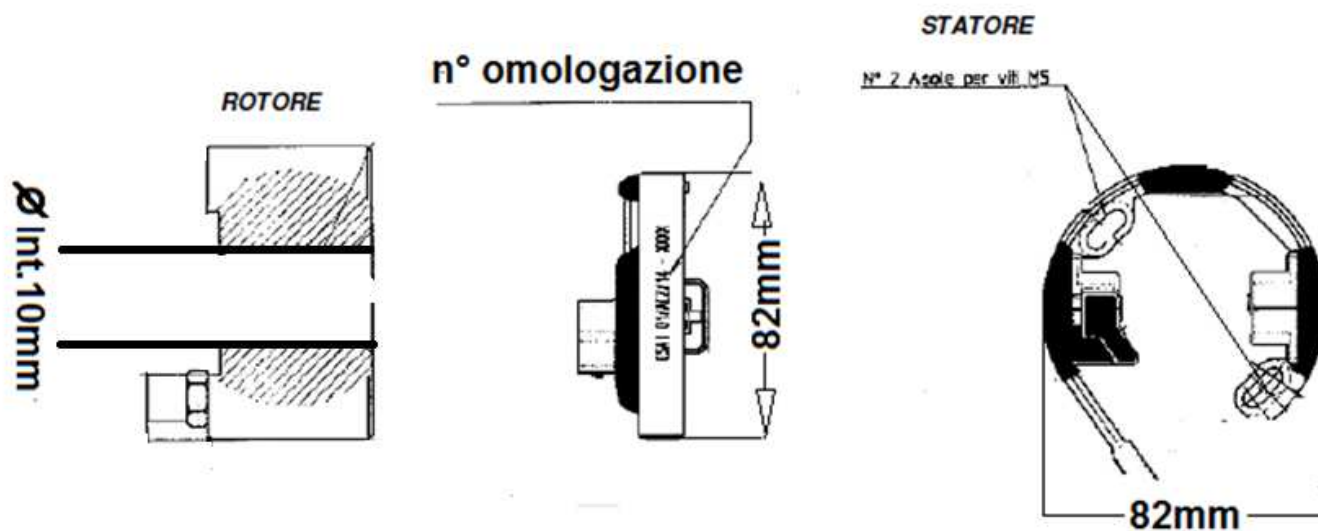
Dimensioni dello statore e del rotore dell'accensione, uniche per tutti
